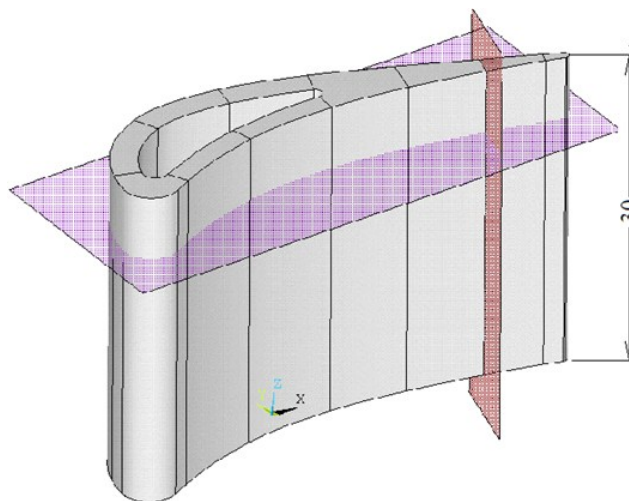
Общий вид монокристаллической лопатки-имитатора и схема изготовления поперечного и продольного сечений
